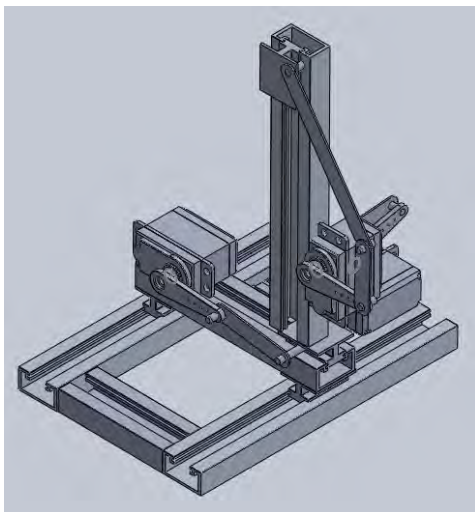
Diseño en SolidWorks del robot cartesiano.
